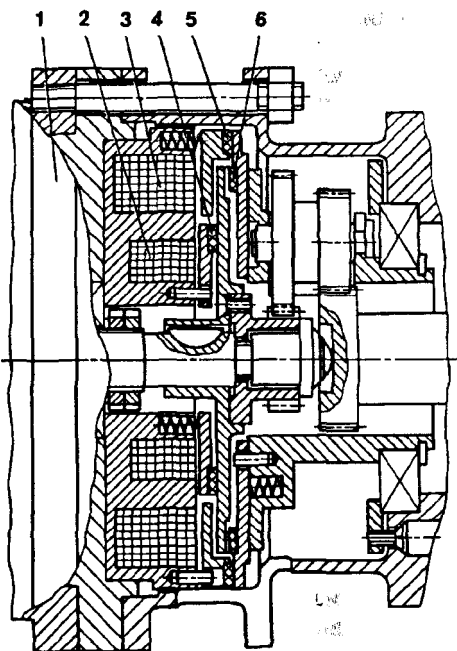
Коробка передач с концентрическим расположением электромагнитов КП и тормоза:
